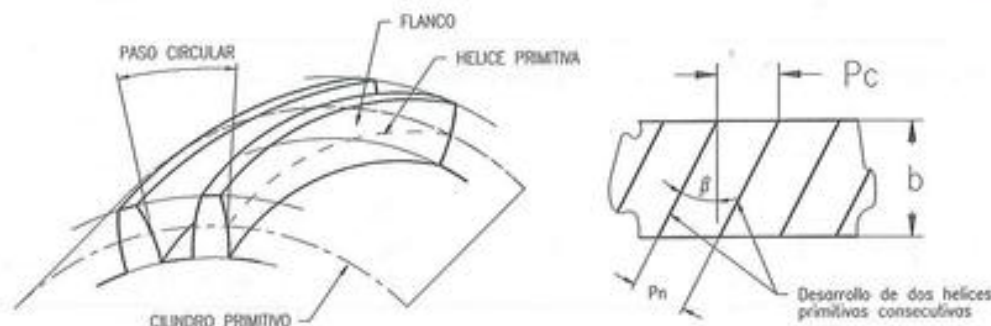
Engranajes cilíndricos helicoidales. Definiciones.
